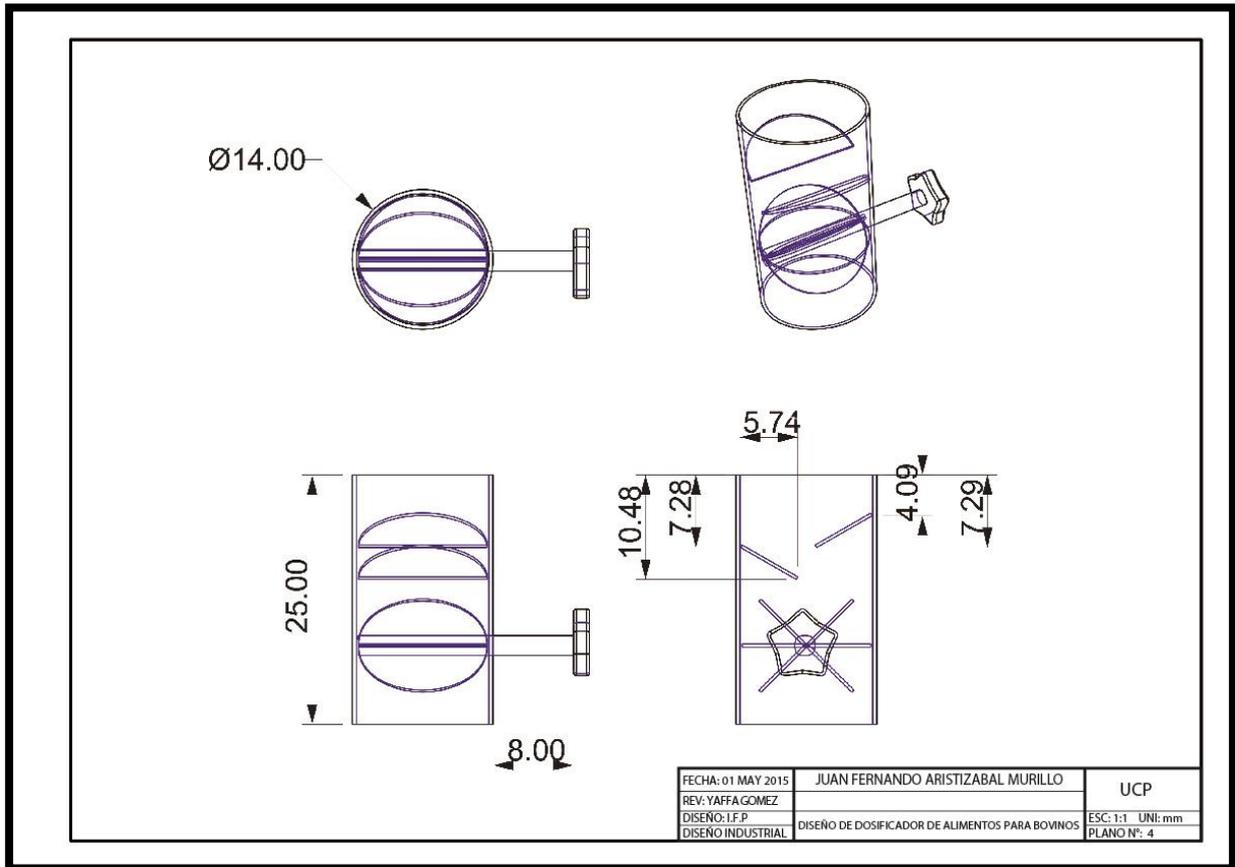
Plano mecanismo. Fuente: elaboración propia
